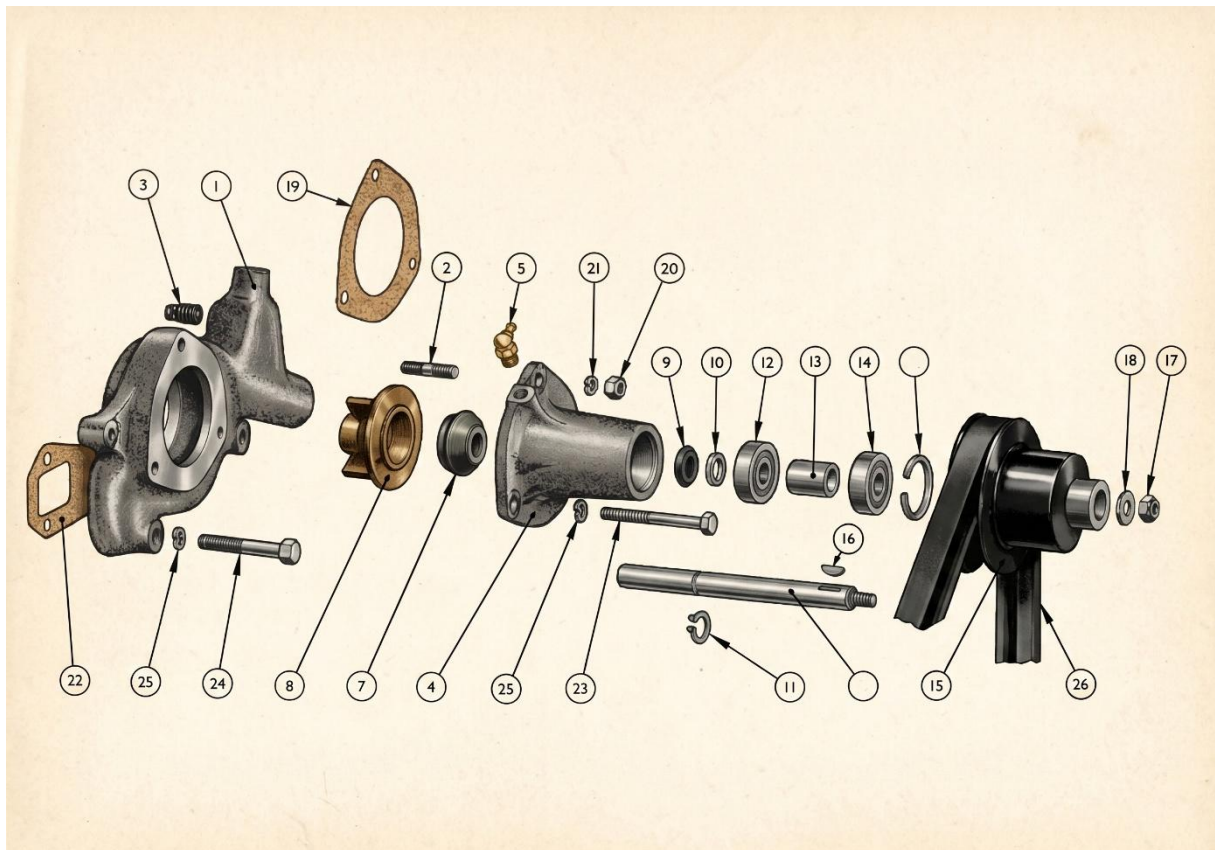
Détails éclatés de l'ensemble du boîtier de la pompe à eau.
